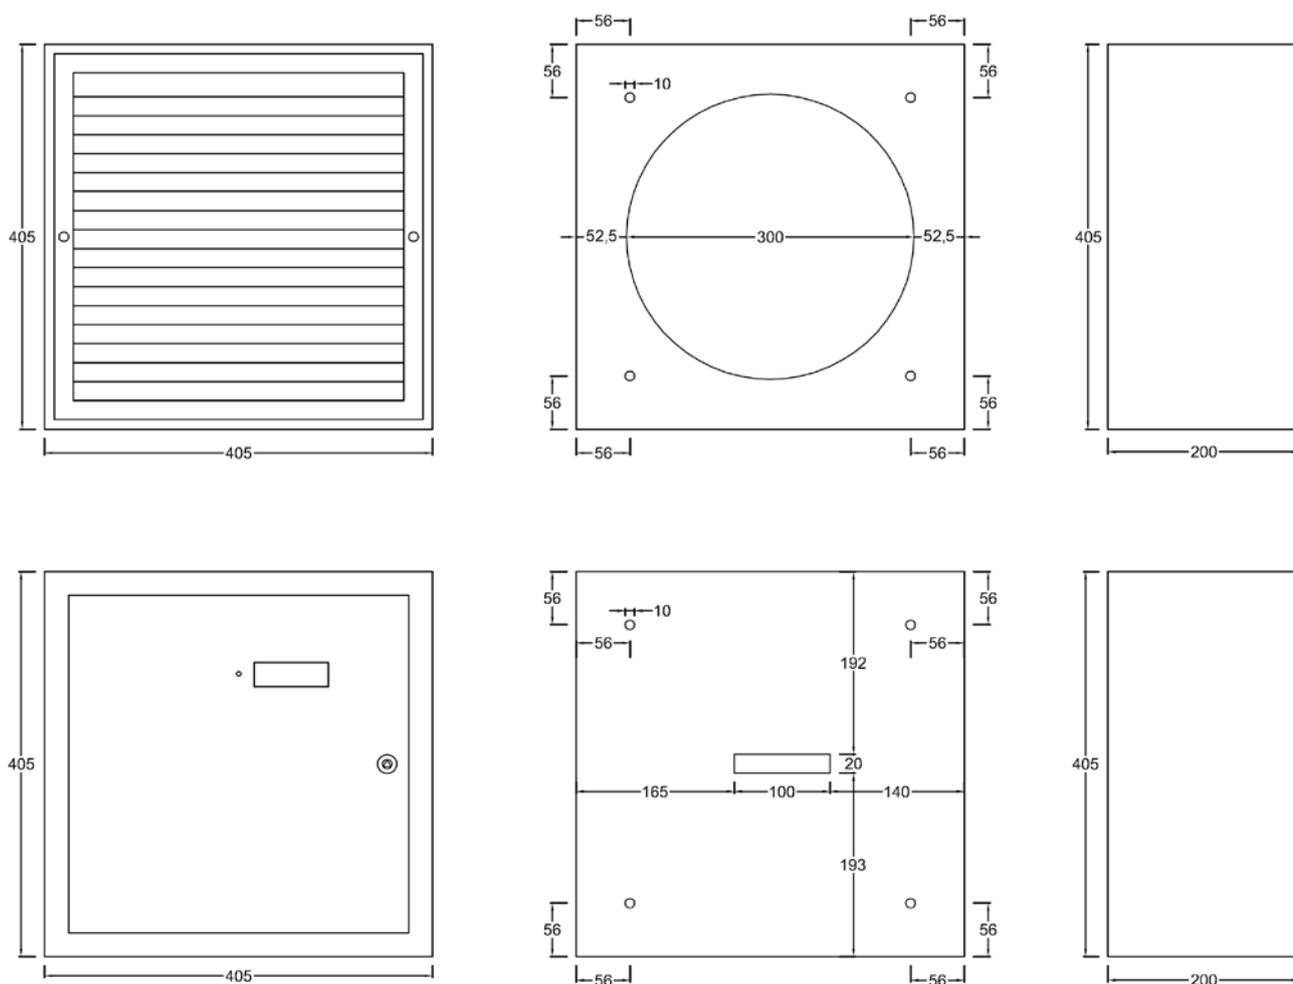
| M500BJ, dimensioni macchina, 2D Model
